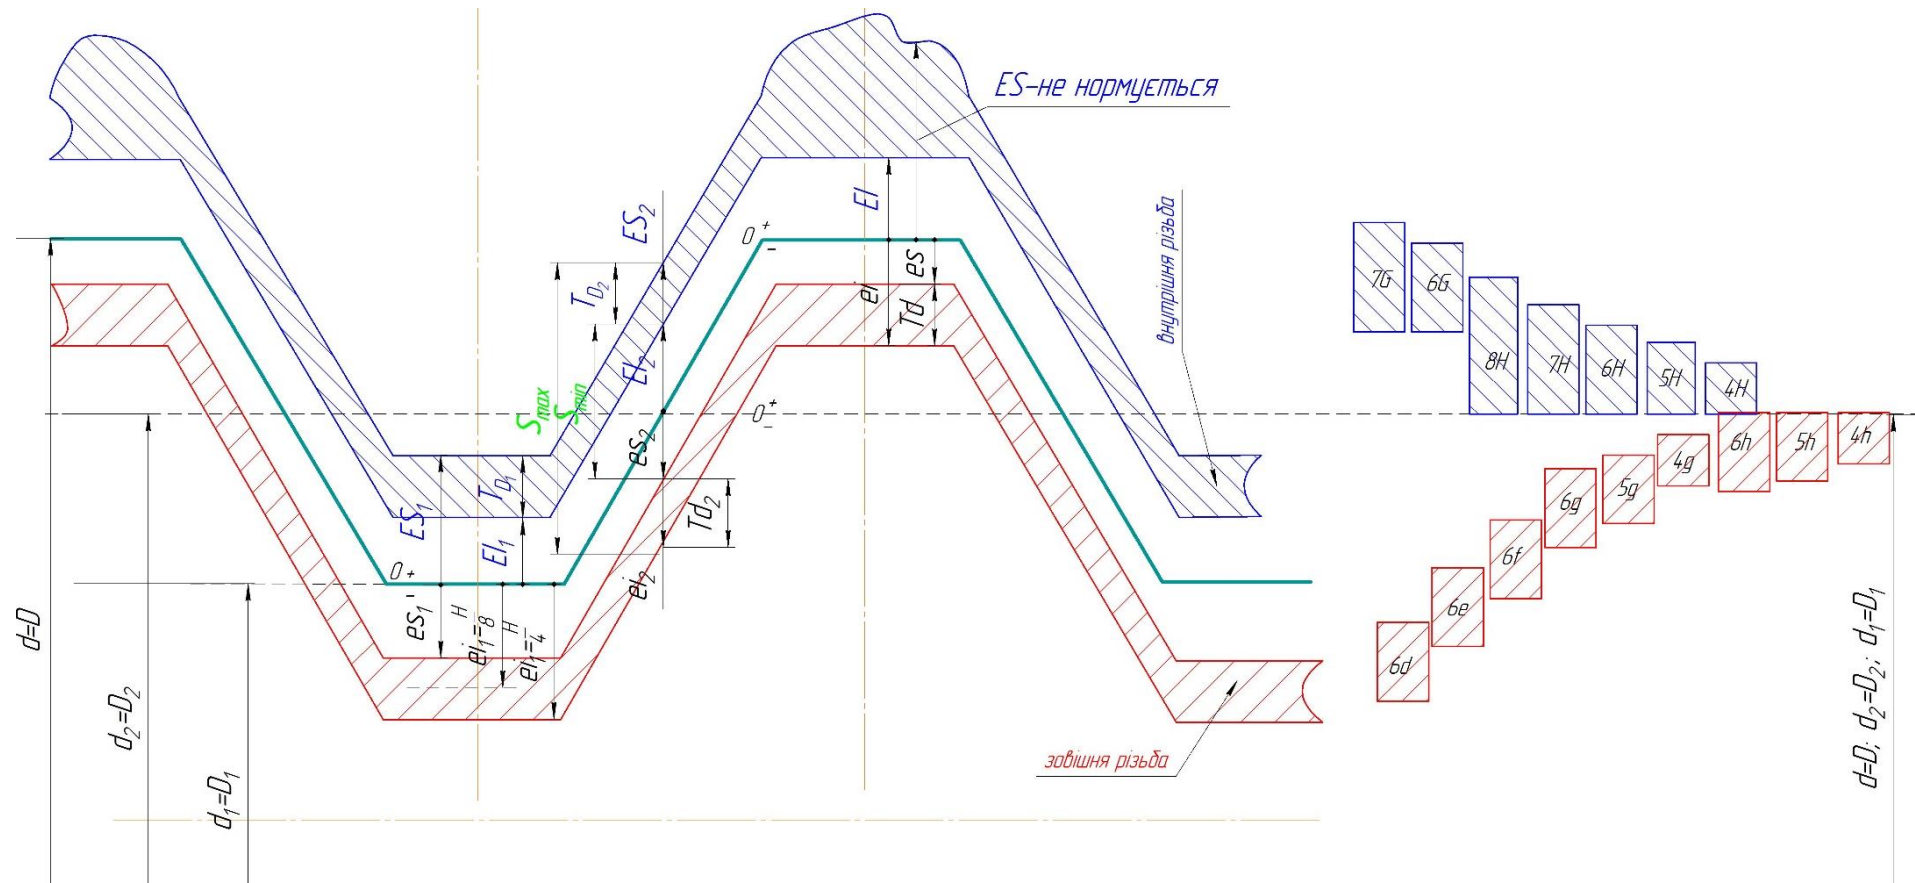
Розташування полів допусків метричної нарізі в посадках з зазором
